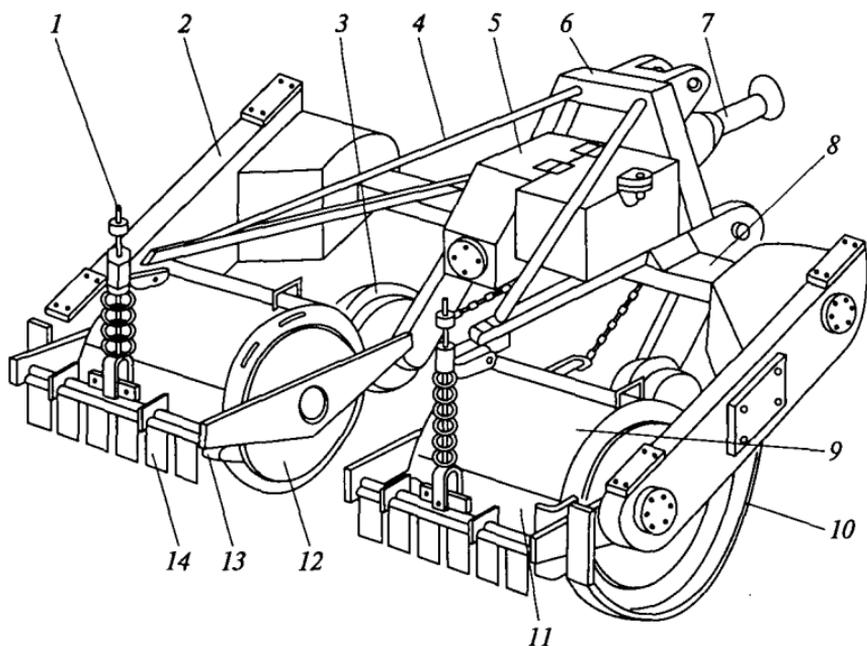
Культиватор фрезерный лесной КФЛ-1,4:
